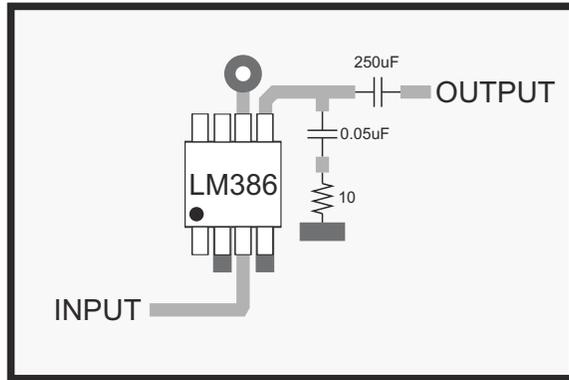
Layout Example for Minimum Parts Gain = 20 dB on SOIC package
